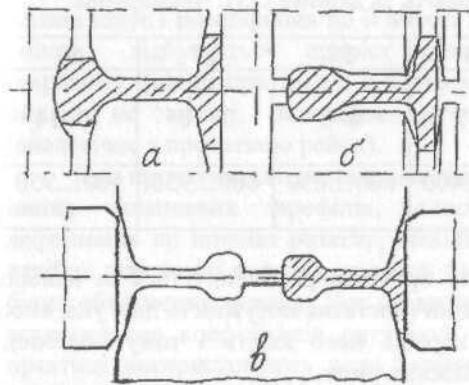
Схема прокатки рейок з використанням багатовалкових калібрів : а-універсальна чотири-валкова кліті; б - допоміжна двохвалкова кліті; в - чистова універсальна кліті з тривалковим калібром.
